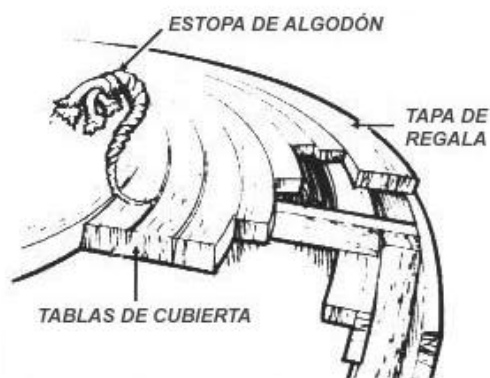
Construcción típica de cubierta y casco con tablazón a tope
